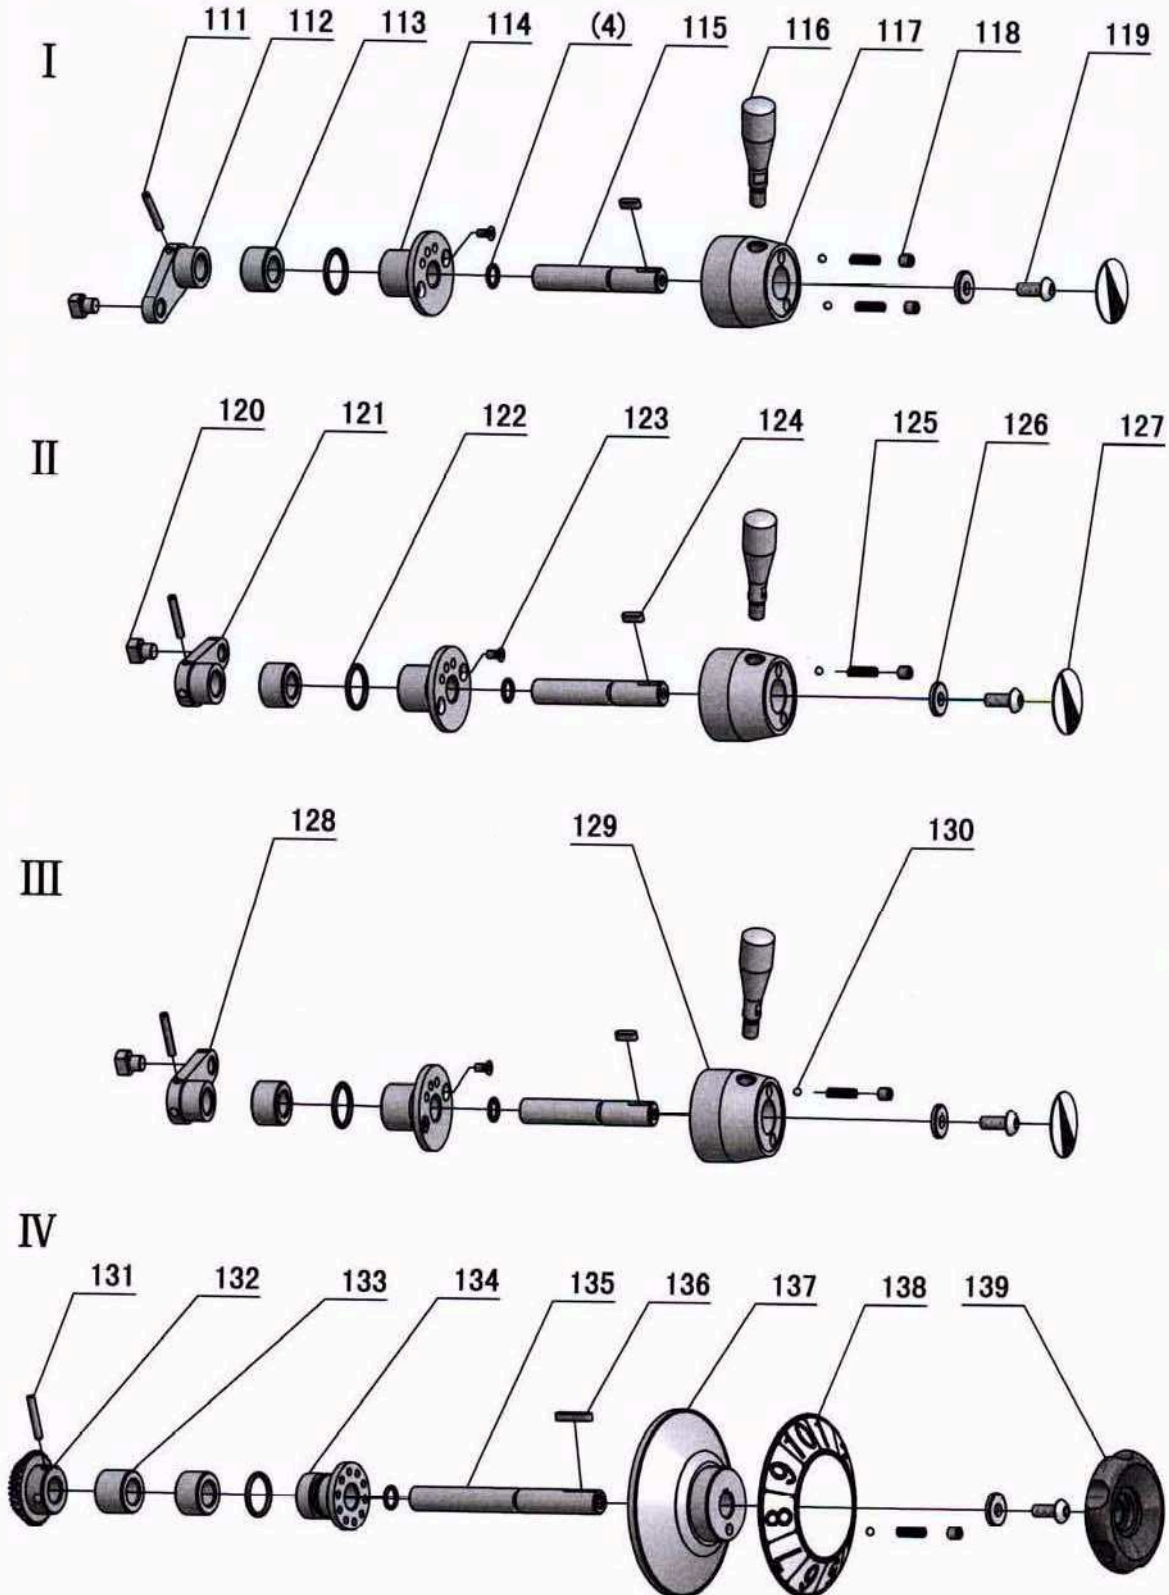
Vorschubgetriebe 4 von 4 - Headstock feed gear 4 of 4
